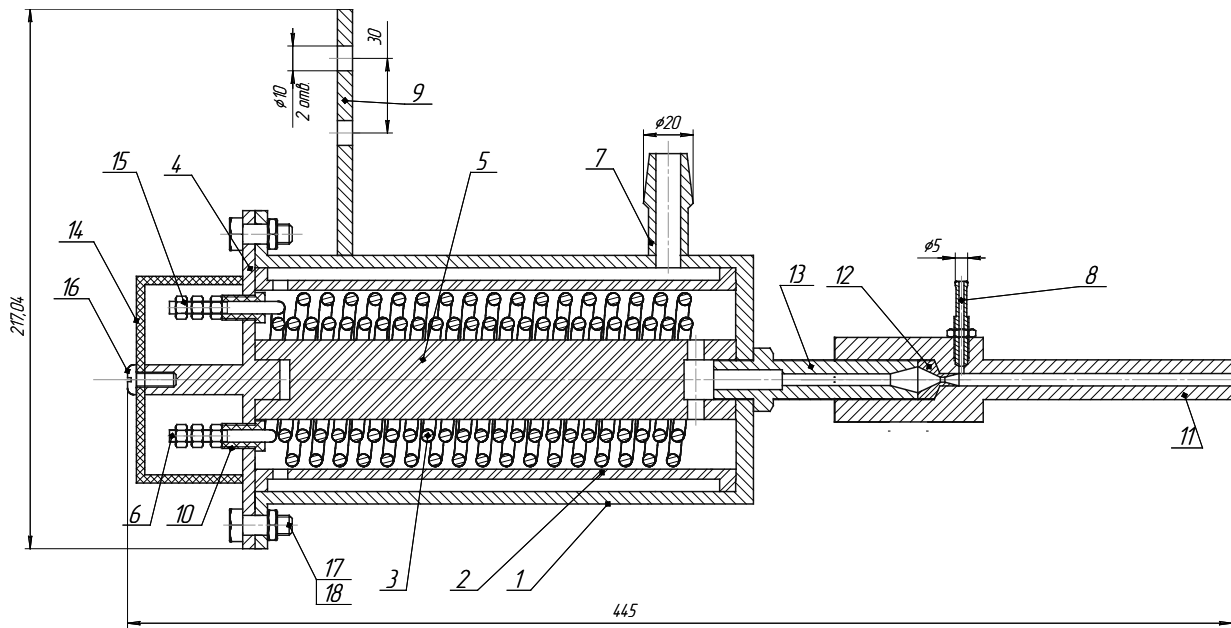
Газодинамічний напилувальний пристрій
